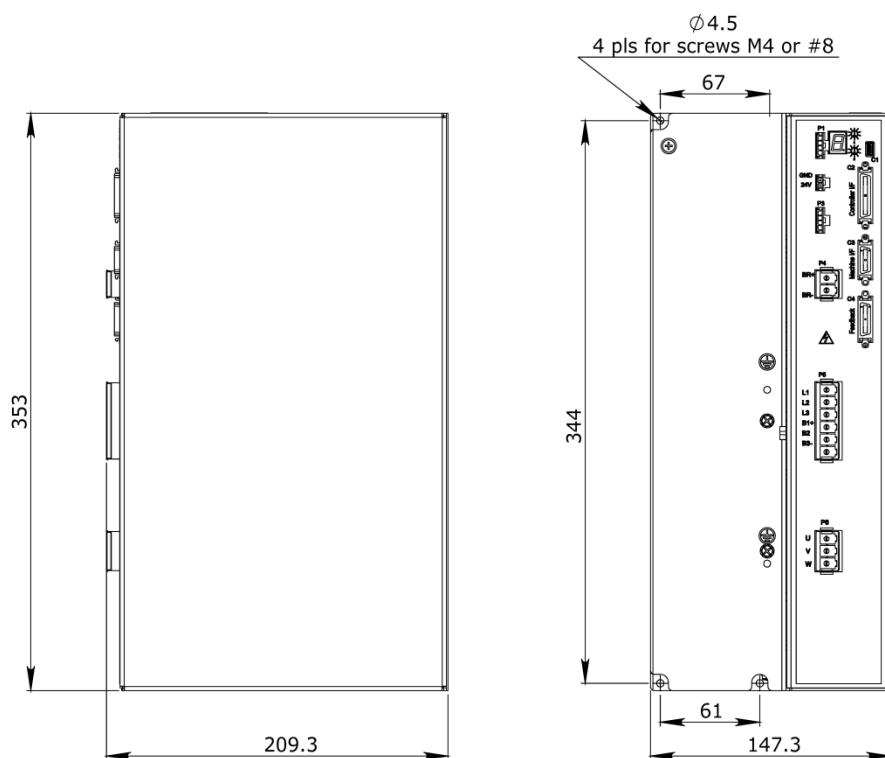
CDHD-024/CDHD-030 (400/480 VAC) – 尺寸 (mm)
